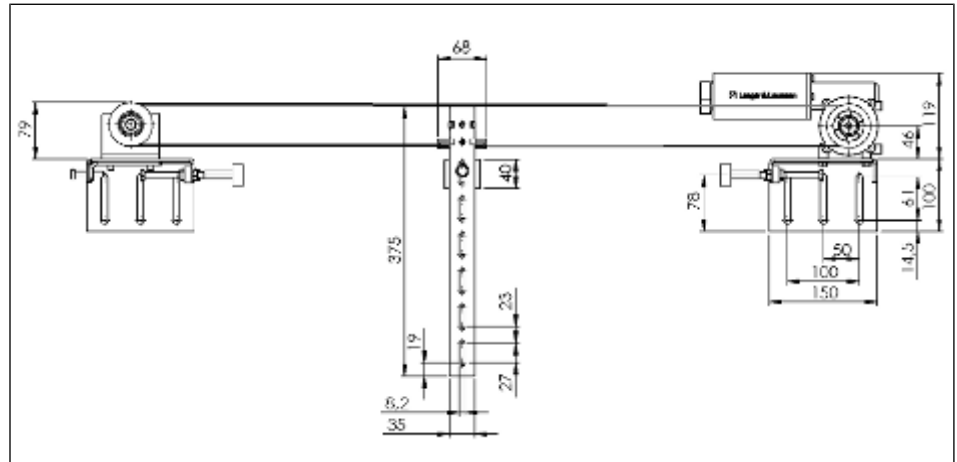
Bemaßung der Mechanik des Türantriebs (Frontansicht) (Angaben in mm)
